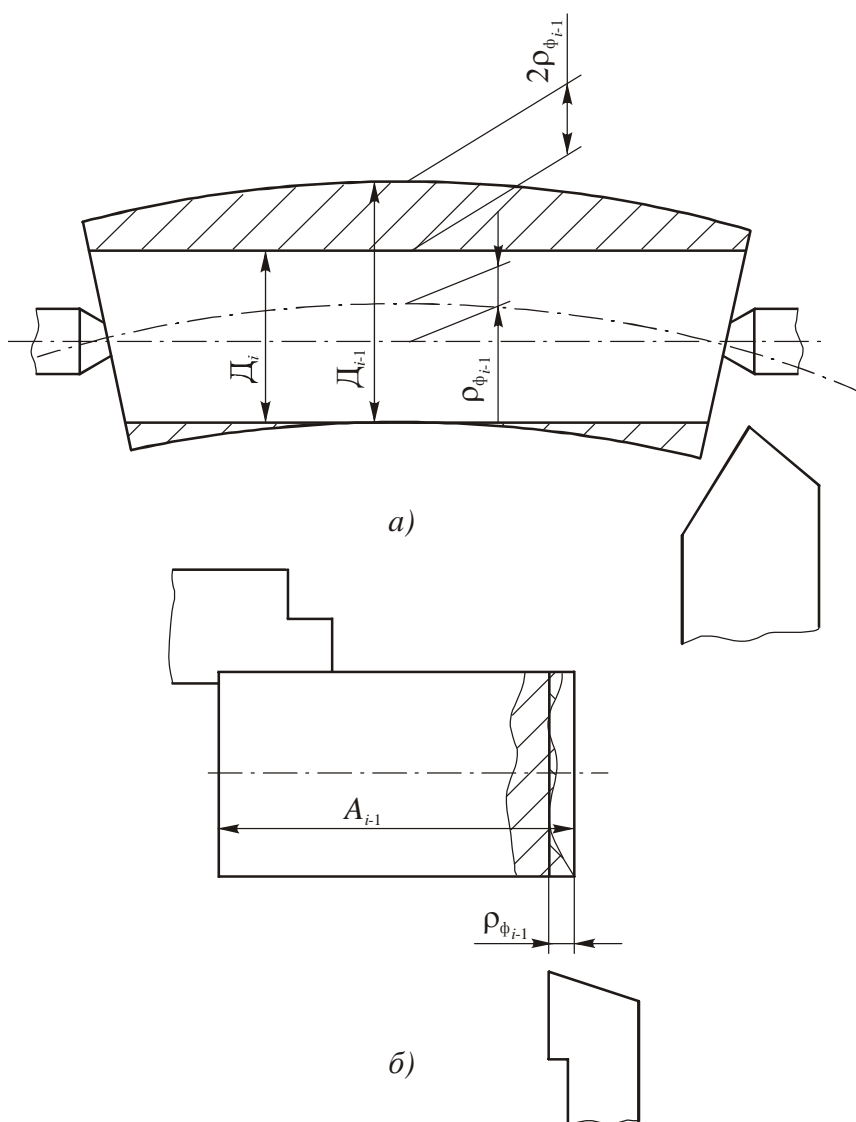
Схемы обработки заготовок, иллюстрирующие влияние погрешности формы обрабатываемой поверхности на величину минимального припуска
